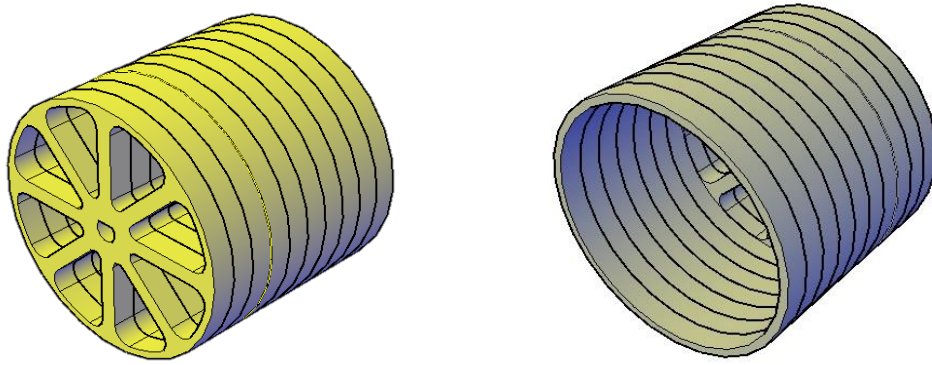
Teker ve Kuyruk Laser Kesim için CAD çizimi
